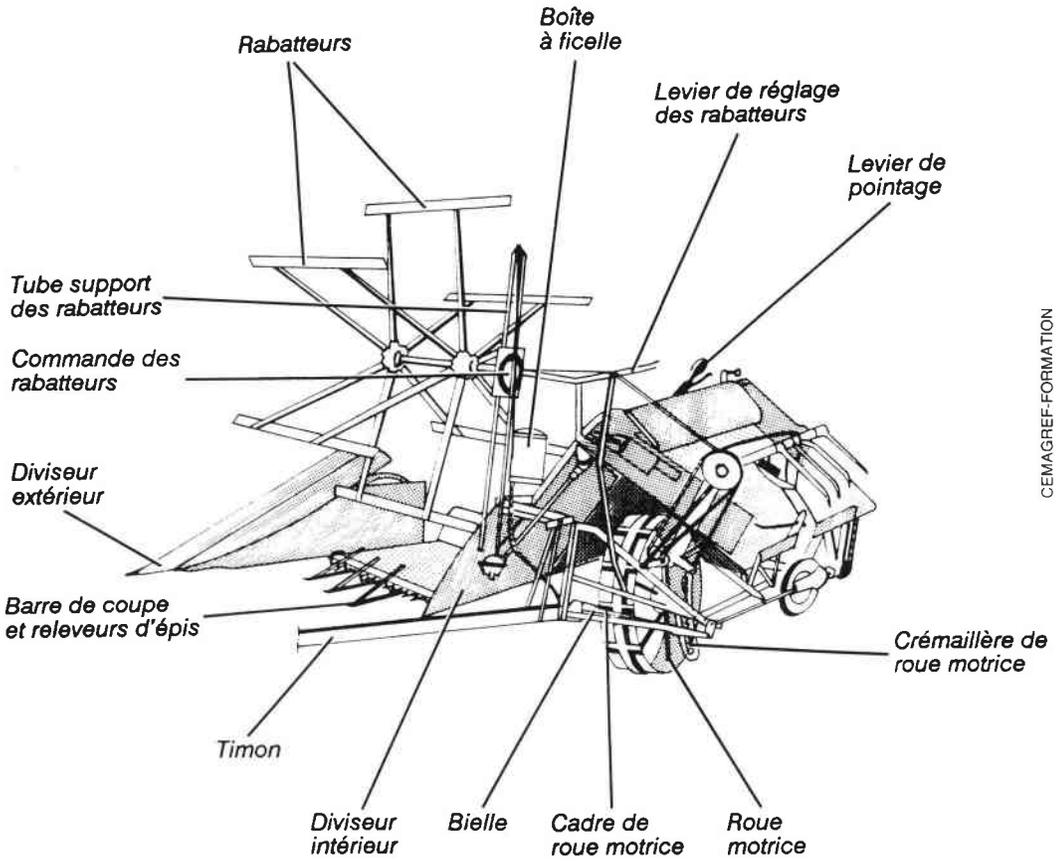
Vue d'ensemble d'une moissonneuse-lieuse.
